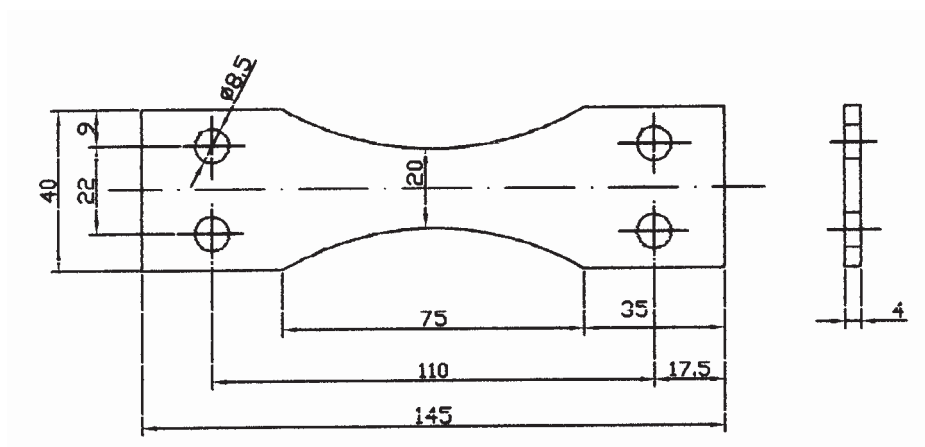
Corpo de prova para o ensaio de fadiga por flexão alternada (conforme – fabricante do equipamento).
